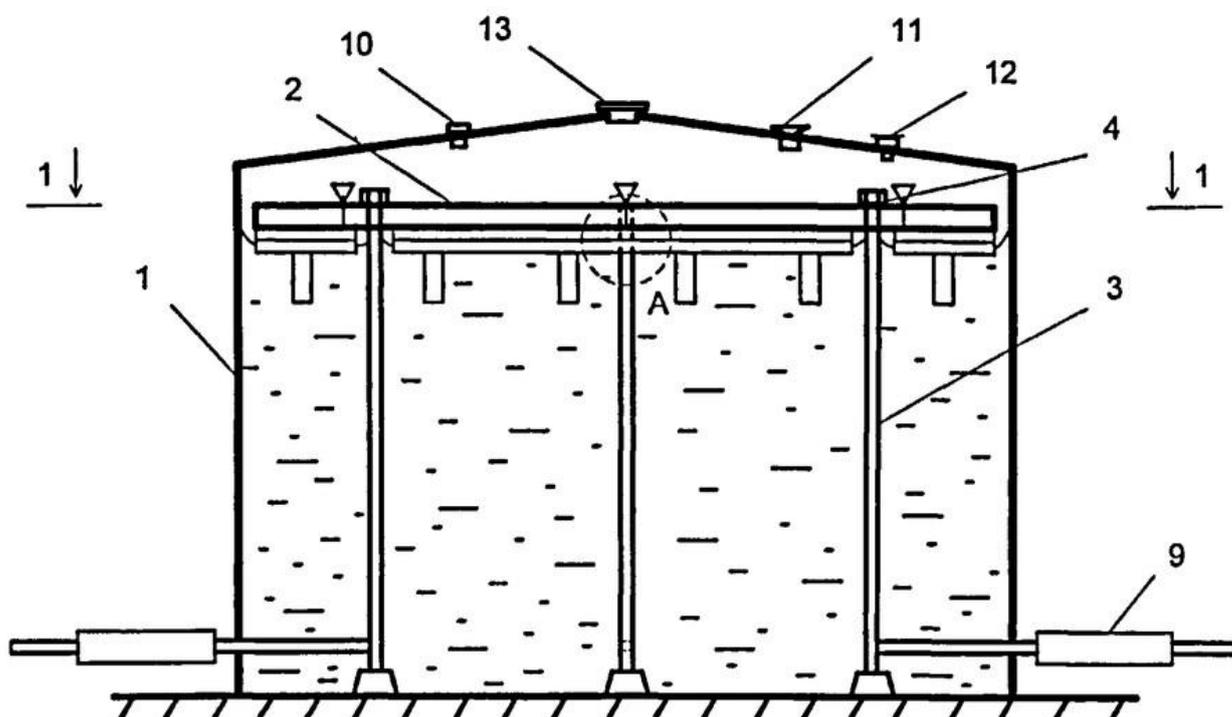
Устройство для тушения горючих жидкостей в вертикальном резервуаре с плавающей крышей или понтоном (общий вид)
